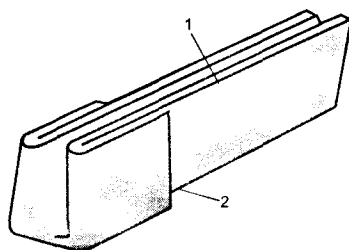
Внешний вид пазовой коробочки с манжетой для усиления: 1 — пазовая коробочка, 2 — отогнутая манжета
